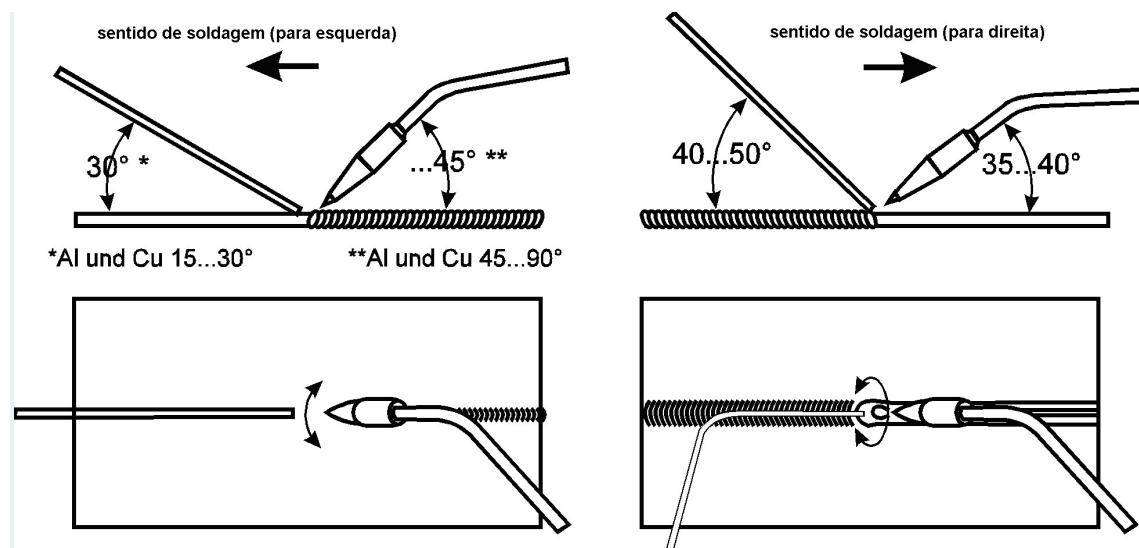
Vista esquemática do método de soldagem para a esquerda e direita
